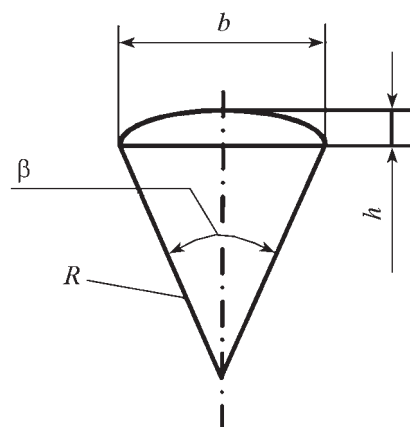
Размеры сварного шва: b – ширина; h – высота; β , R – угол и радиус сегмента
